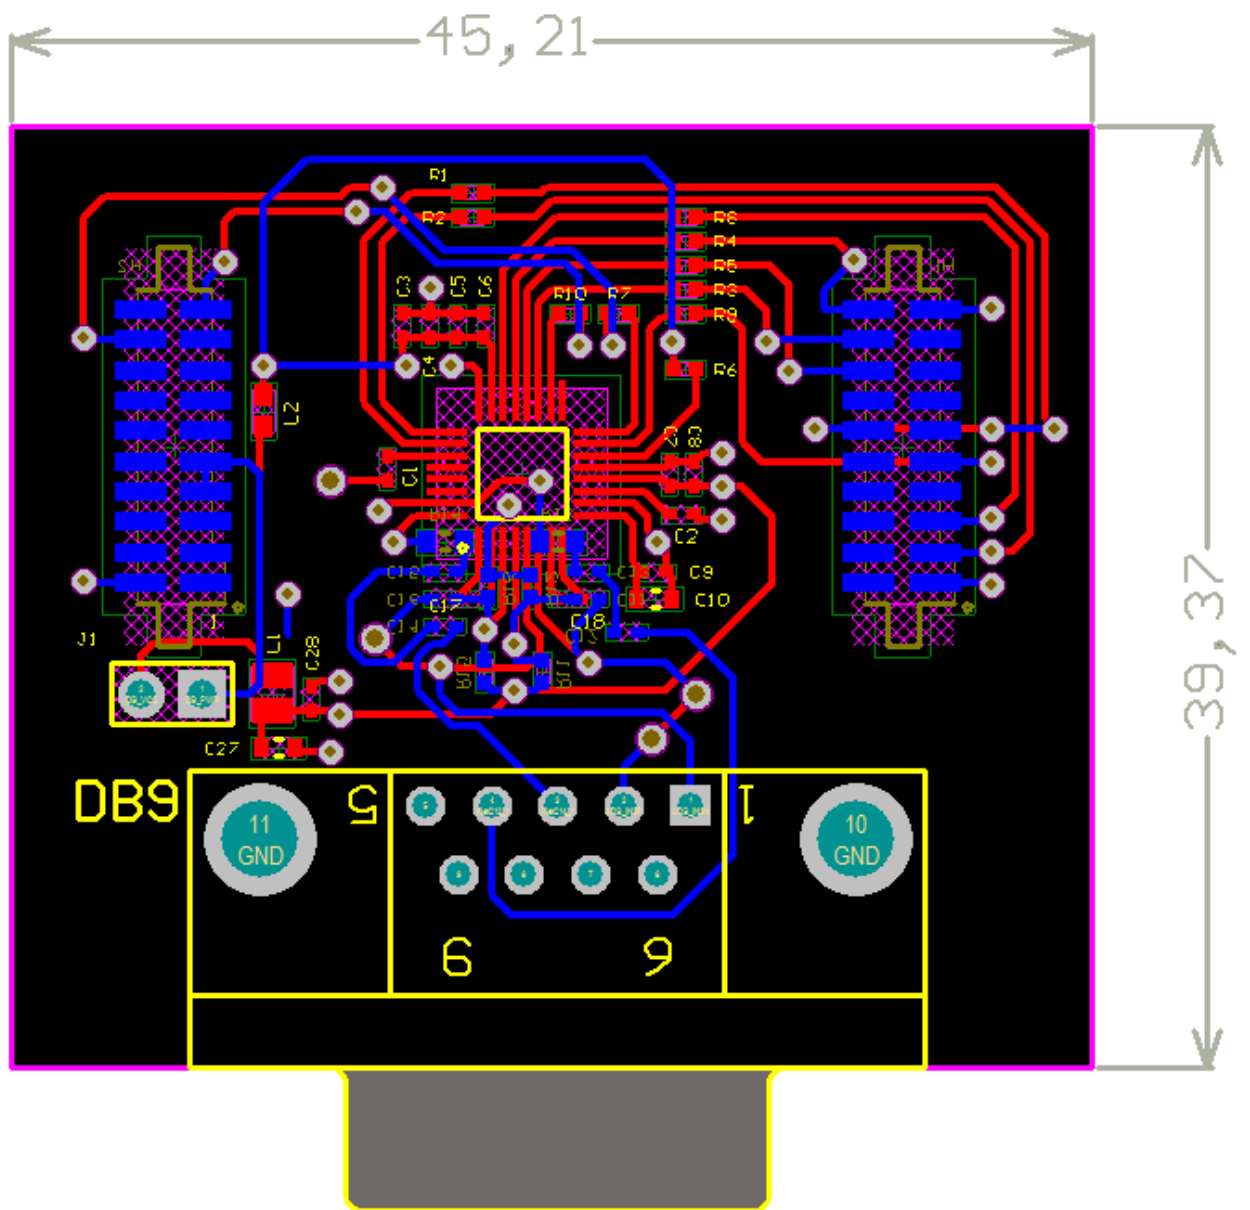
Diagrama del PCB (Rojo: Pista capa superior, Azul: Pista capa inferior), Dimensiones PCB: 45,21mm x 39.37mm
